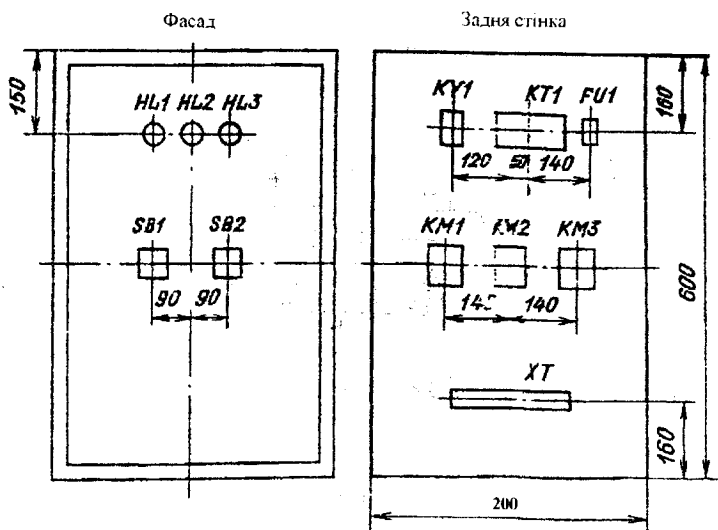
Схема розташування, або загальний вигляд щита з компоновкою електрообладнання
